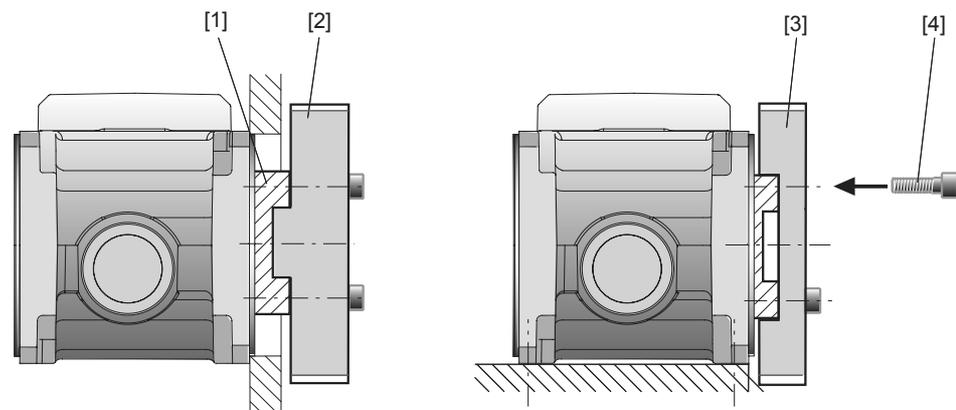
esempio di montaggio BSBF.. - blocco flangia 53425AXX
